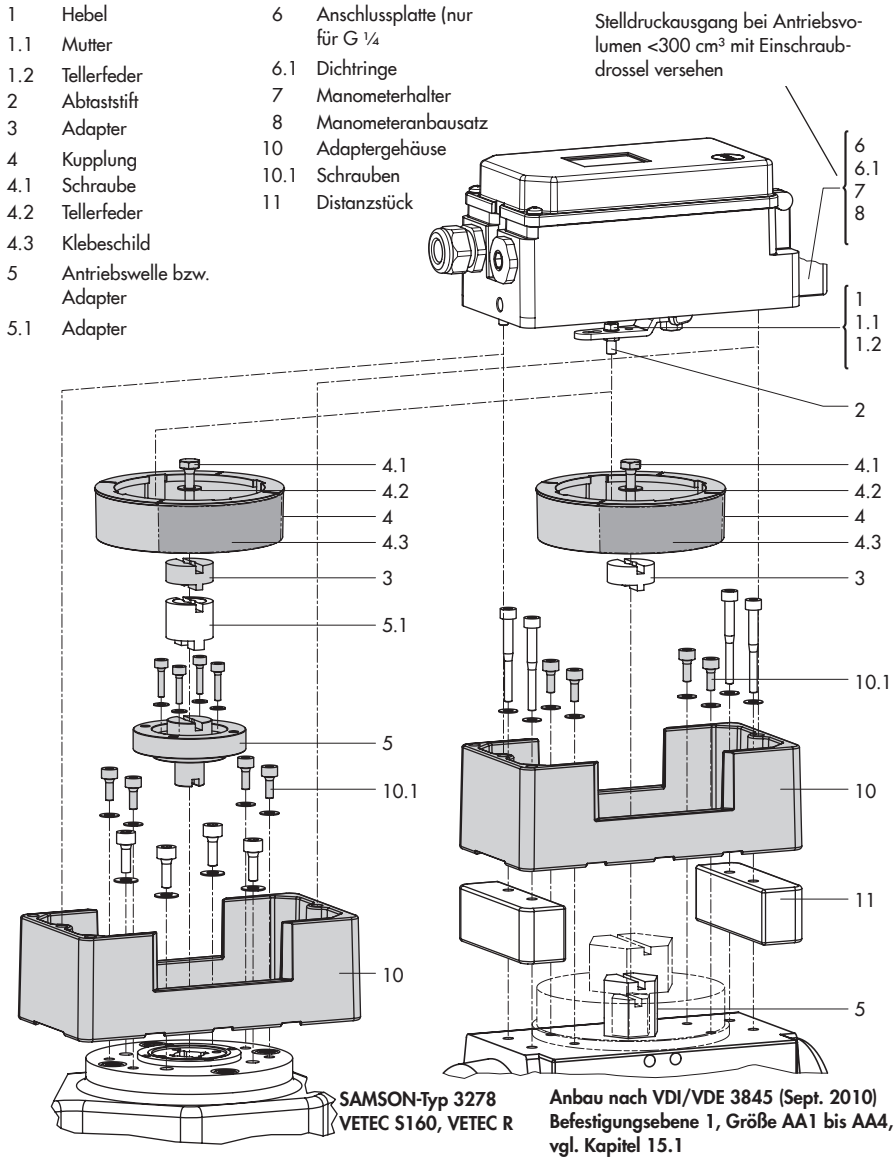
Anbau an Schwenkantriebe, schwere Ausführung
